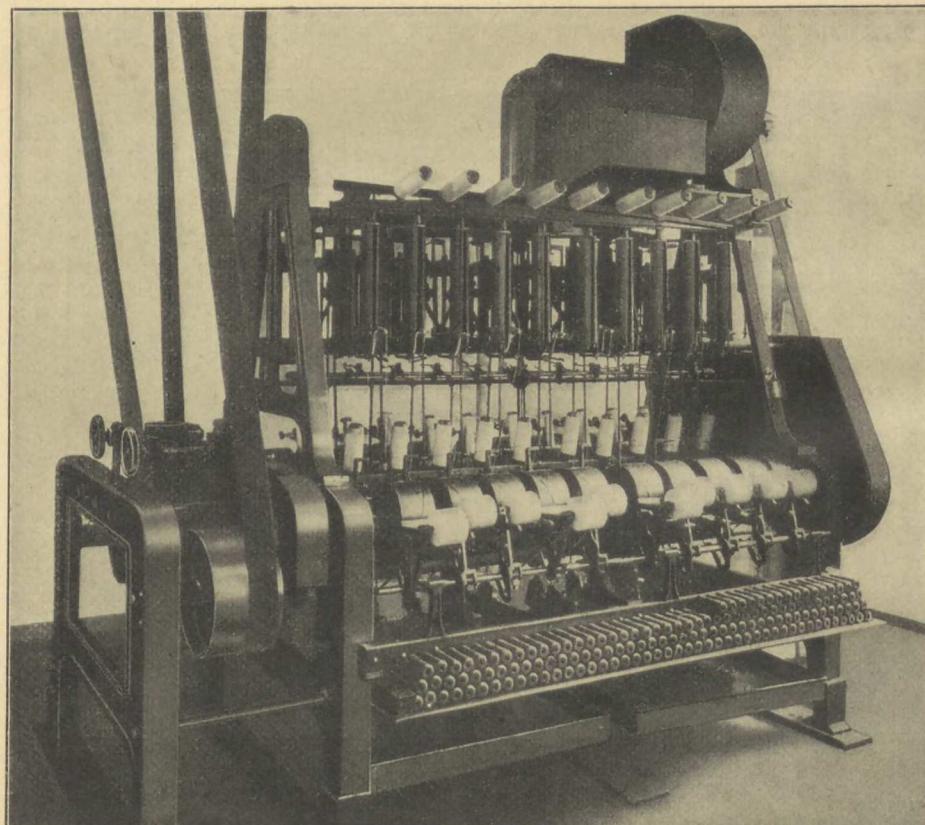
Garn-Sengmaschine mit Gasheizung.
